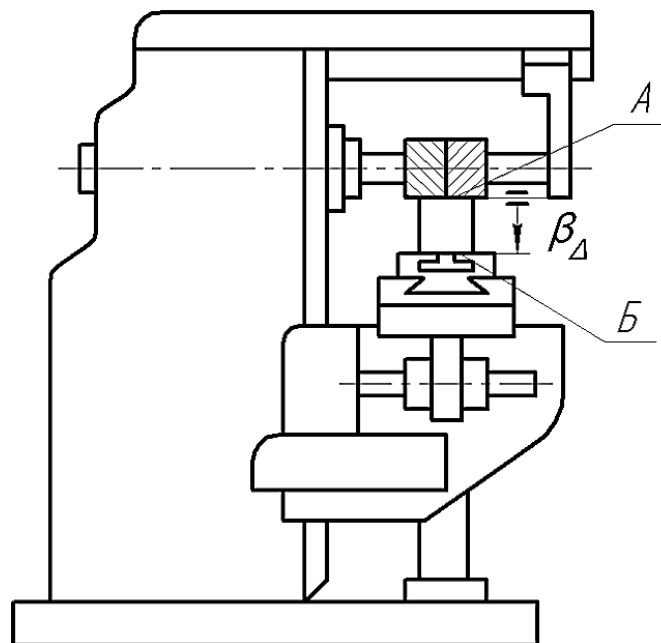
Схема оброблення деталі на універсально-фрезерному верстаті
